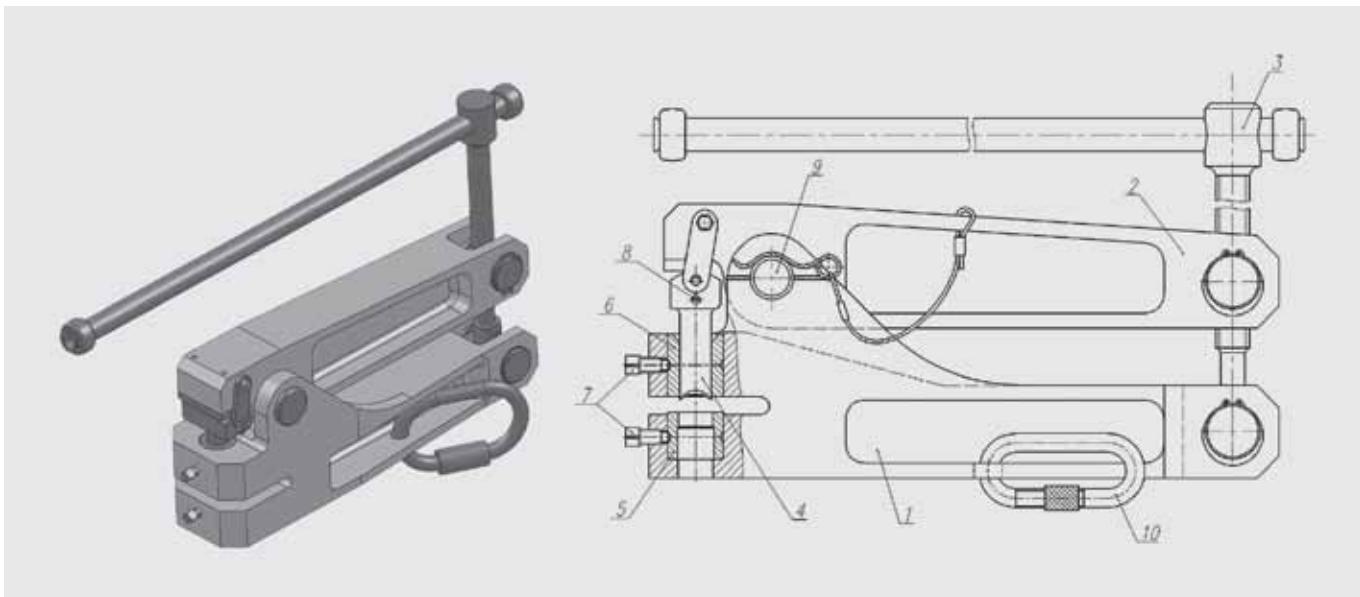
Конструкция пробойника: 1 — корпус; 2 — рычаг; 3 — винтовой механизм; 4 — пуансон; 5 — матрица; 6 — обойма пуансона; 7 — винты стопорные; 8 — винты крепления пуансона; 9 — ось; 10 — карабин такелажный
